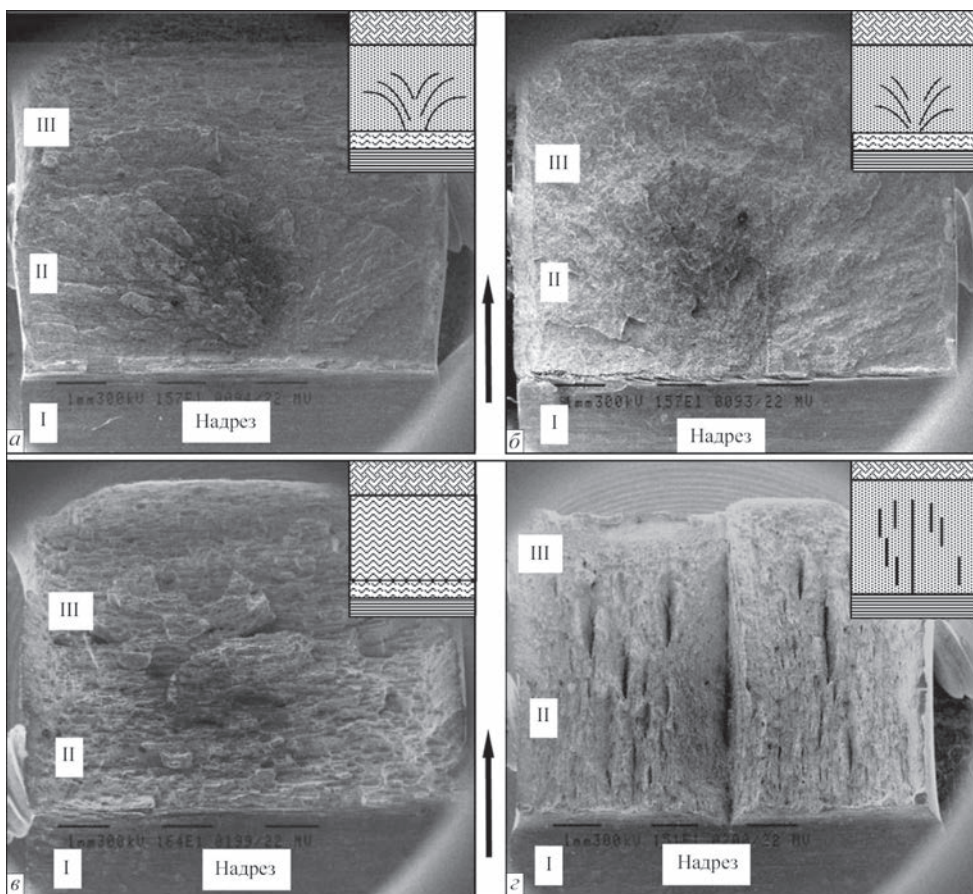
Общий вид поверхности изломов по зонам разрушения образцов, изготовленных из: сварного соединения (а); обработанных по ТЦС заготовок (б); валиковой пробы (в); основного металла (г), $\times 16$ (в верхней правой части кадров схематическое изображение изломов) (обозначения см. в тексте)
